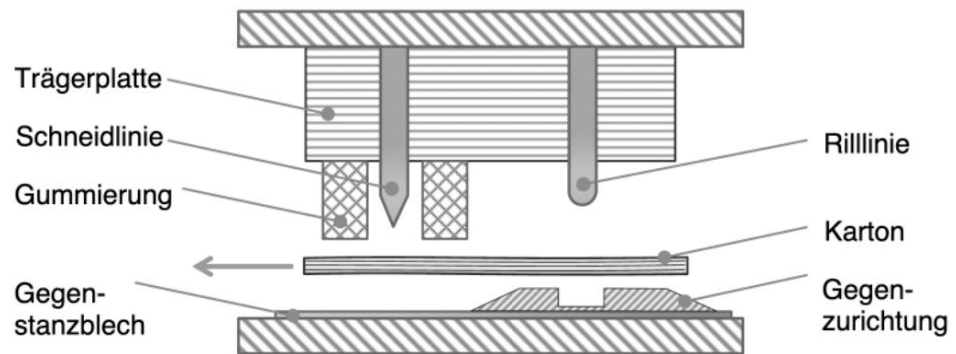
Werkzeuggeometrie und -komponenten [17]
